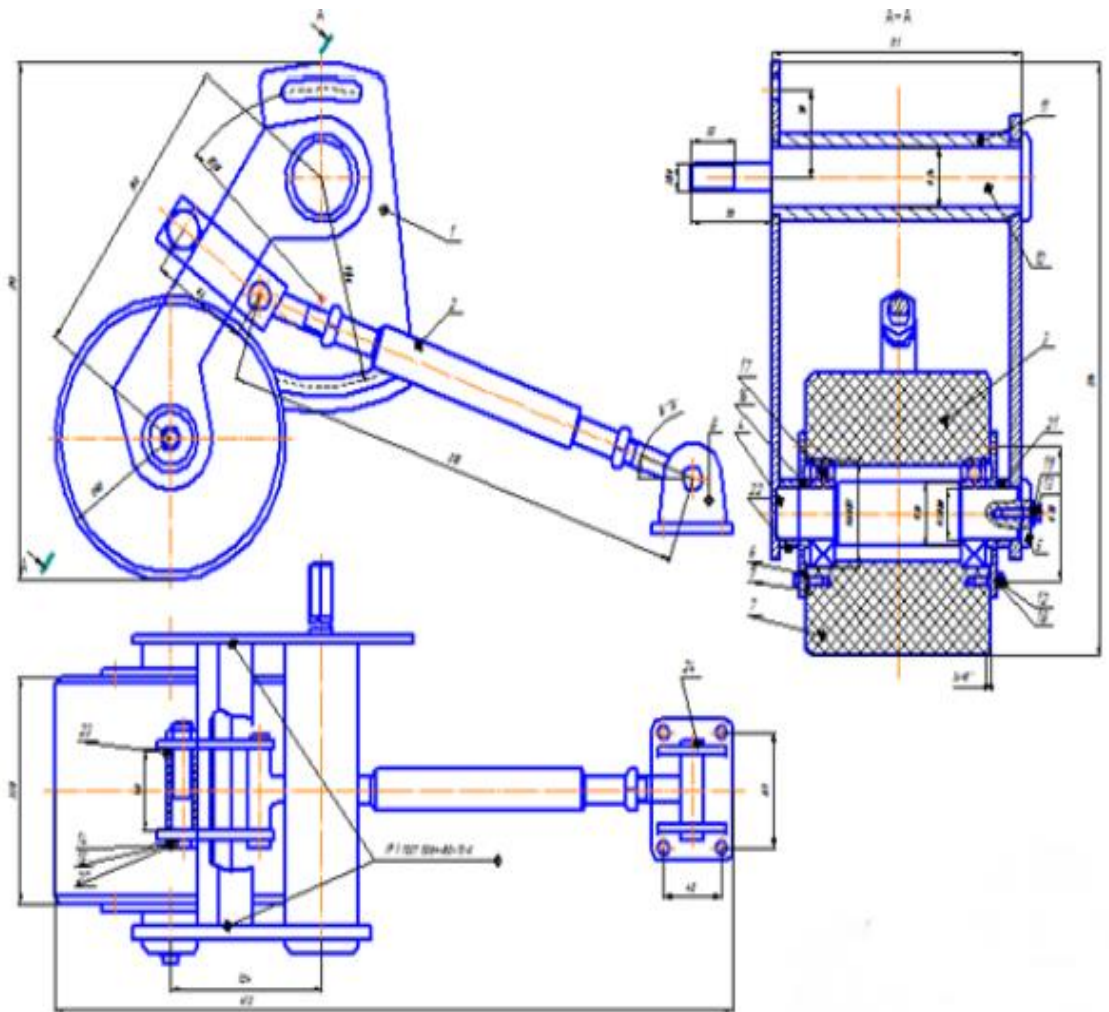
Натяжний пристрій 1 – натяжний пристрій; 2 – тягм; 3 – ролики; 4 – вісі; 5 – кільце; 6 – кришка; 7 – бобиш; 8 – стійка; 9 – проклад; 10 – вісі; 11 – трубі; 12, 13, 14 – болти; 15 – гайки; 16 – манжеті; 17 – підшипн; 18, 19, 20 – шайби; 21, 22, 23 – втулки; 24 – штефт.
